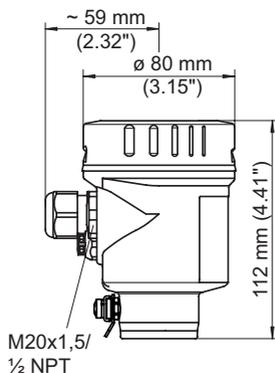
Корпуса в исполнении IP66/IP68 (0,2 bar), (с установленным модулем индикации и настройки корпус выше на 9 mm/0.35 in)
